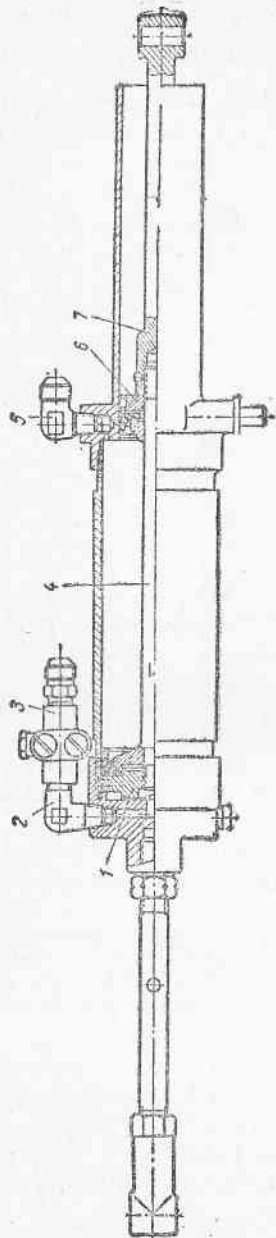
Дверной механизм автобуса ЗИЛ-158
